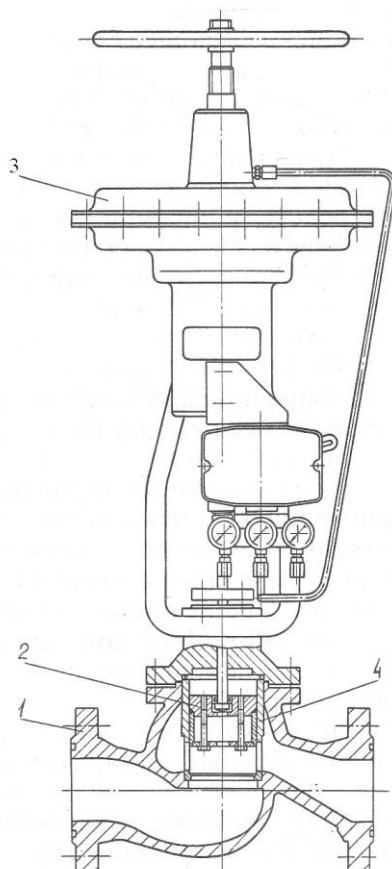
Регулирующий клапан: 1 – корпус; 2 – плунжер; 3 – пневмопривод; 4 – стакан
